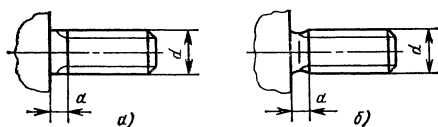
Форма недореза при выполнении наружной метрической резьбы:
